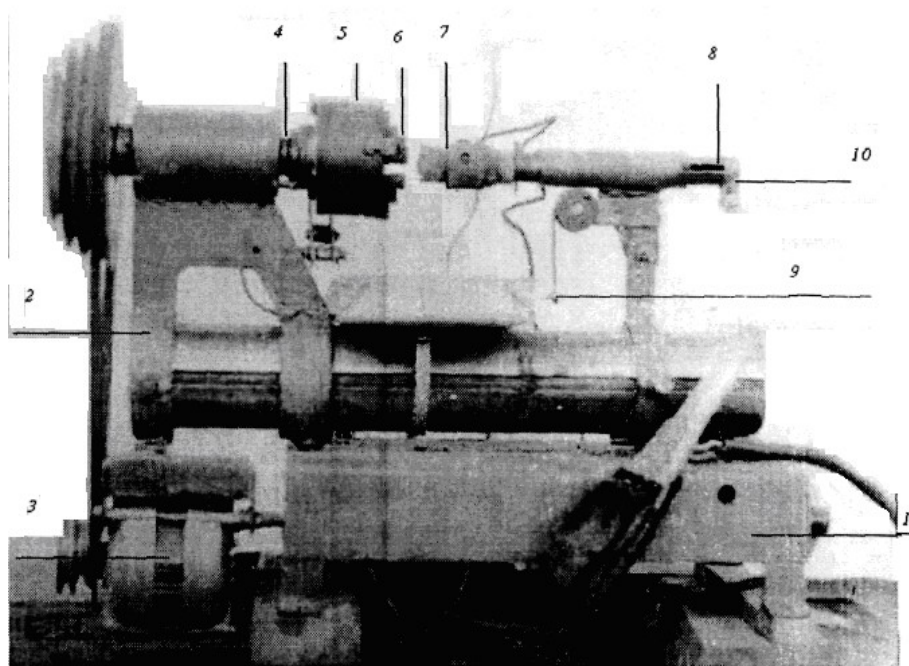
Установка для нанесения покрытий на образцы натирием на базе токарного станка.
